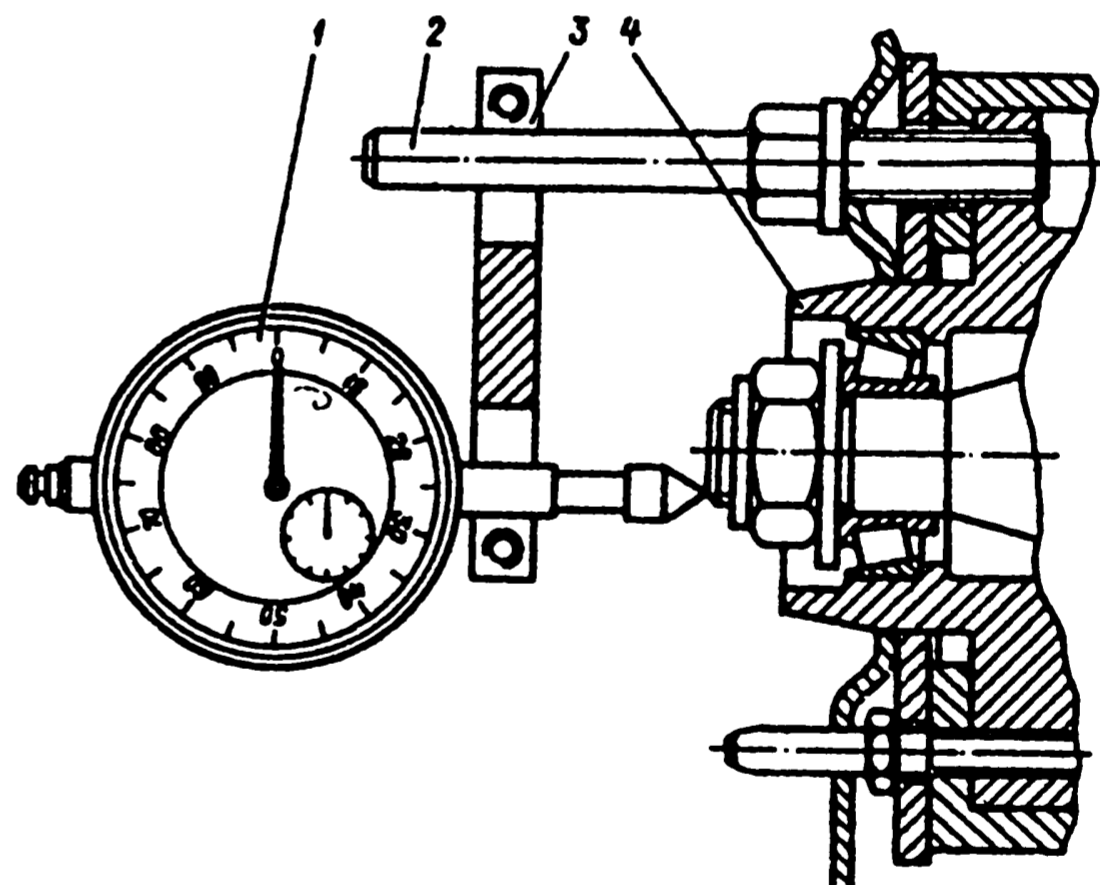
Проверка осевого зазора подшипников ступицы переднего колеса приспособлением 02.7834.9505: 1 - индикатор; 2 - болт; 3 - кронштейн; 4 - ступица
